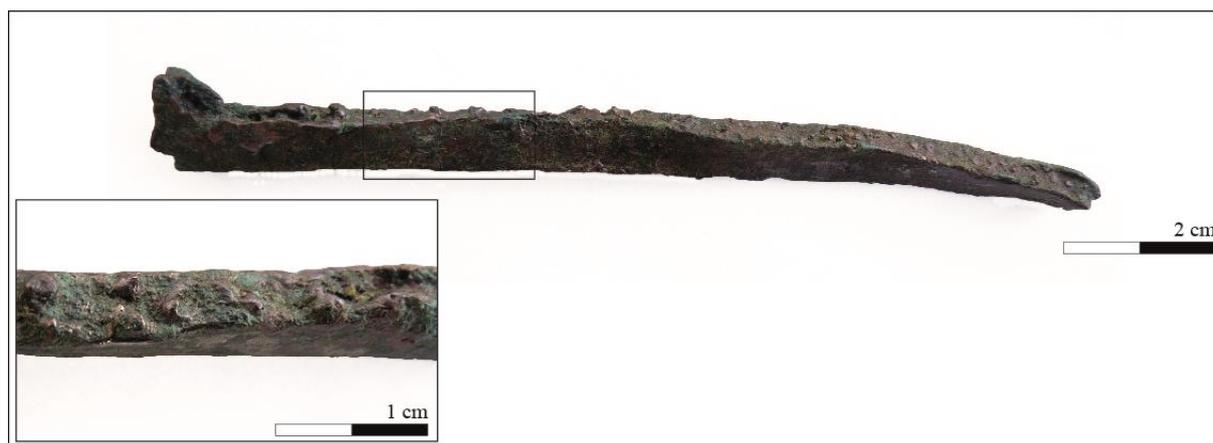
chute de découpe d'une ébauche brute de fonderie destinée au martelage, de 4 mm d'épaisseur, détail de la barbe brute de fonderie (Impasse Conguay, fouilles INRAP, RO L. Vermard). (Photos L. Saussus)
